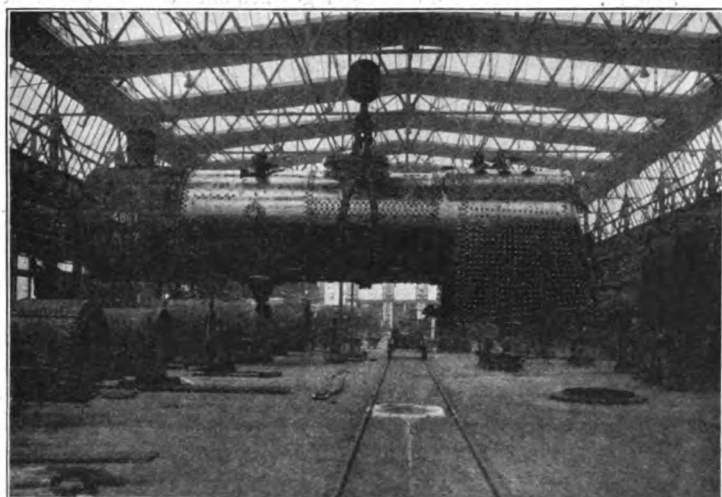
Kesselschmiede; Blick in der Längsrichtung.
